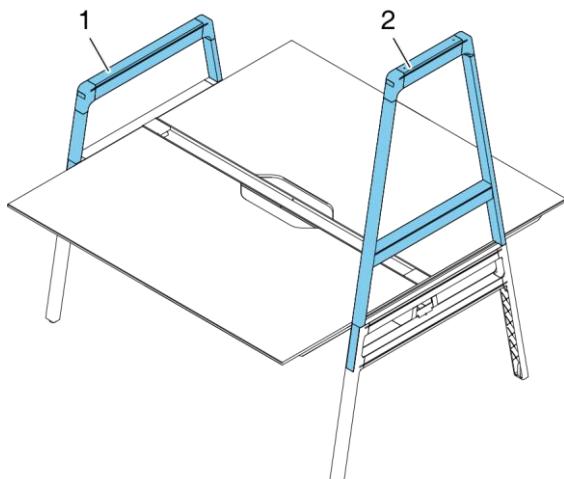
Archi rialzati, variante postazione di lavoro doppia
